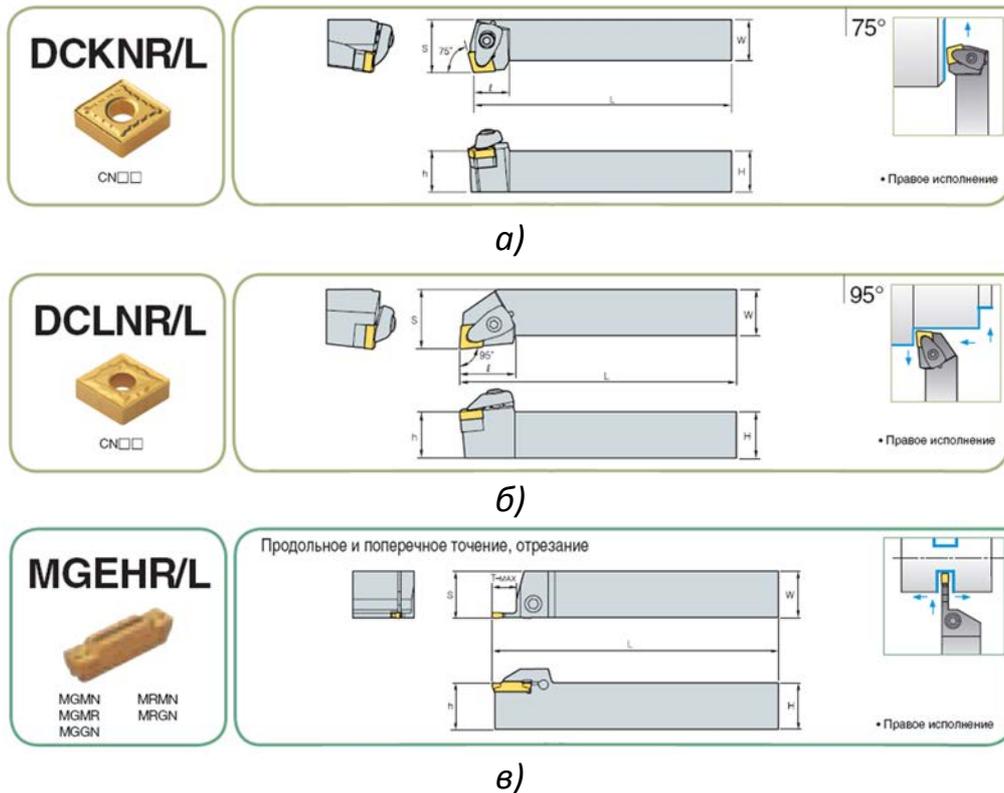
Токарные резцы «Korloy» для станка с ЧПУ
